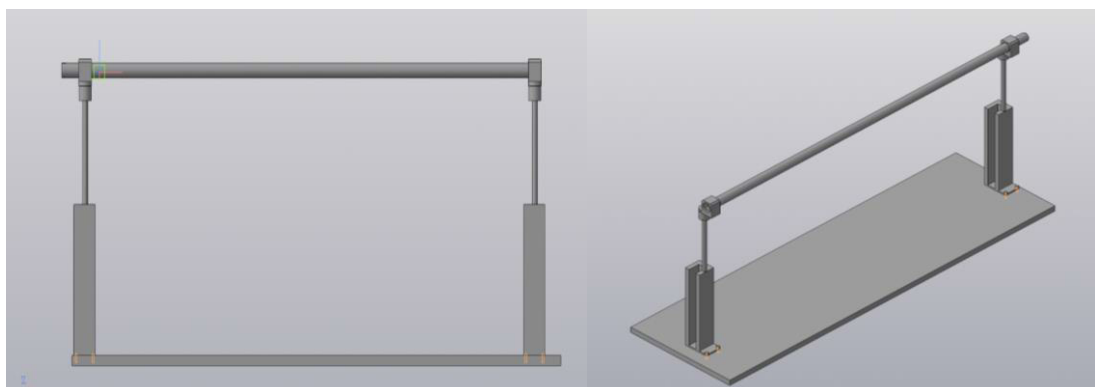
Фрагмент сборки направляющей трубы автомата на поддерживающих опорах
